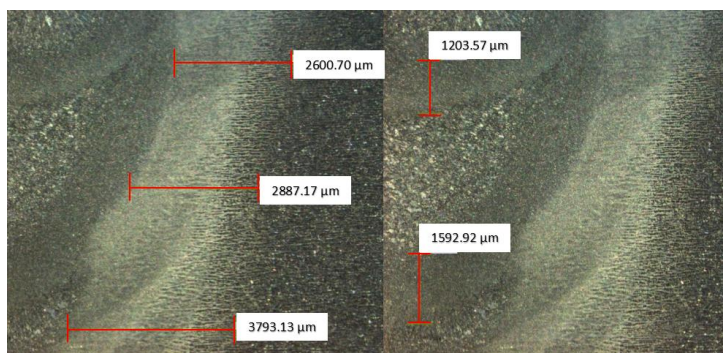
Unión soldada por el proceso GMAW, H.I. = 2.9 KJ/mm. Medición del ancho de la ZAC y de la profundidad del metal de soldadura recristalizado.
